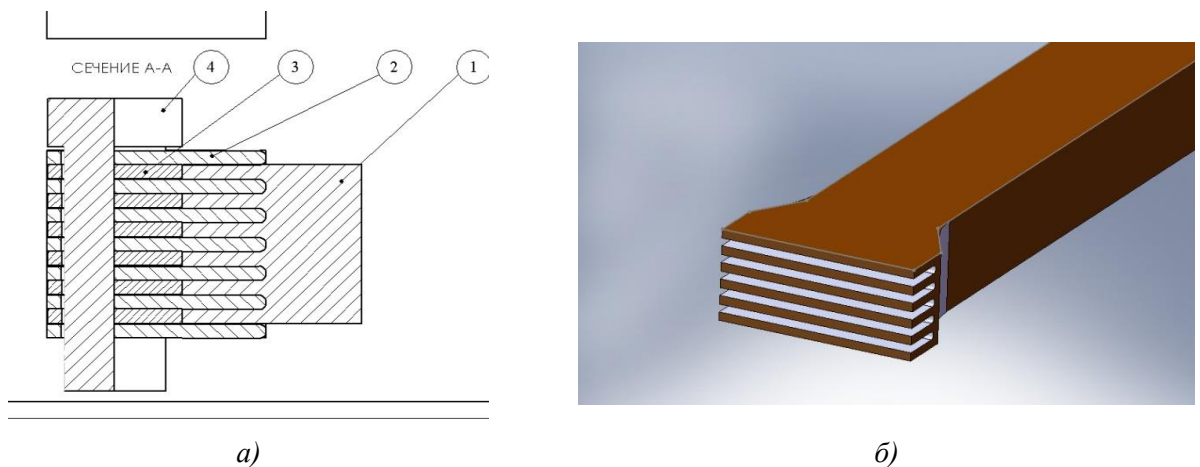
Схема закрепления- (а): 1-образец, 2-захват, 3- вставка, 4- крепёжный элемент. (б): Внешний вид образца для испытания
